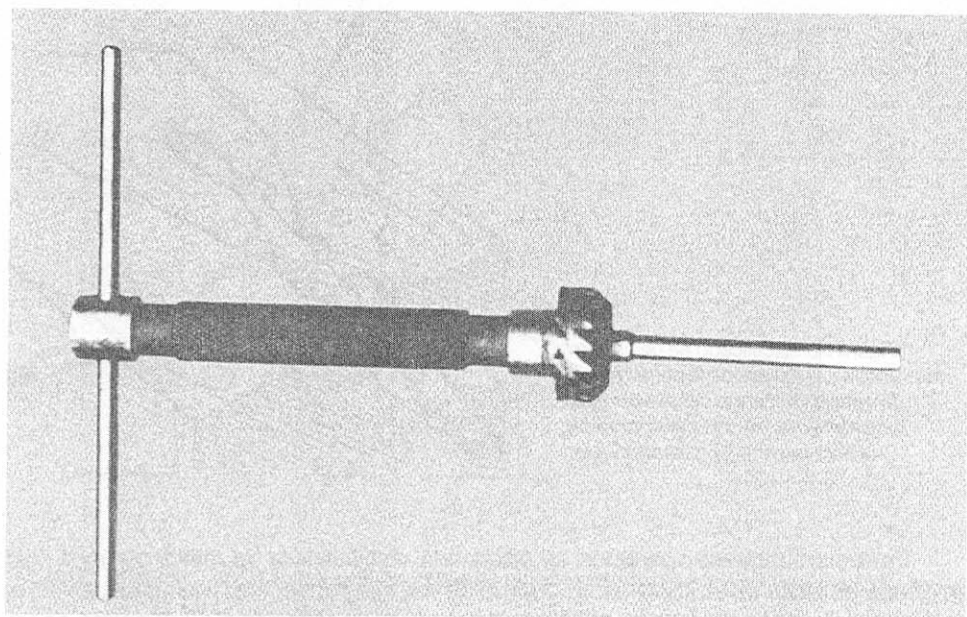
Herramienta apta para el fresado de los asientos de válvula.
